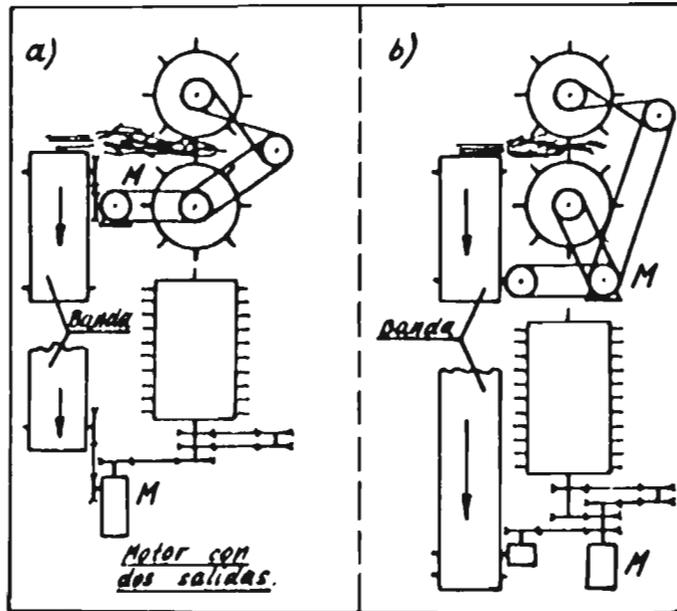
Esquemas cinemáticos de la máquina desmolidora accionada por un solo motor: M: es la posición del motor.
